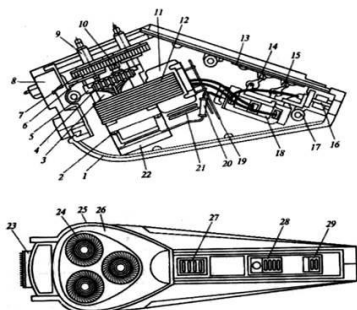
Электробритва «Харьков-65»: 1, 25 – полукорпуса; 2 – винт; 3 – якорь; 4 – амортизатор; 5 – станина; 6 – рычаг кулисы; 7 – зубчатые колеса; 8 – стригущий блок; 9 – поводок; 10 – шестерня; 11 – катушка; 12 – пакет статора; 13 – направляющая пластина; 14, 15 – рычаги; 16 – штырь вилки; 17 – стойка; 18 – переключатель напряжения; 19 – печатная плата; 20 – конденсатор; 21 – резистор; 22 – колодка; 23 – подвижный нож; 24 – неподвижный нож; 26 – корпус ножевого блока; 27 – движок фиксатора ножевого блока; 28 – движок выключателя; 29 – движок переключателя.
